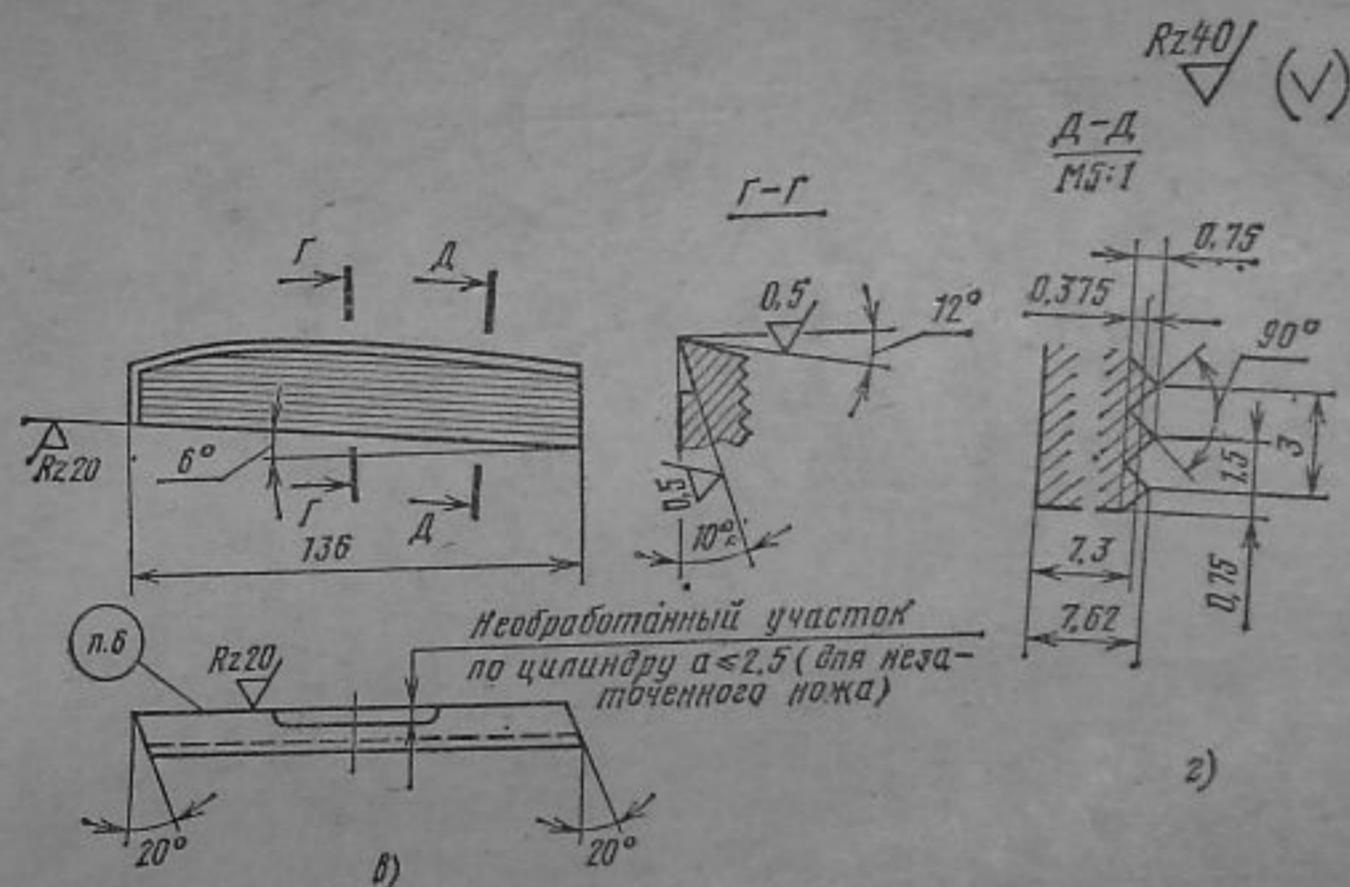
Чертеж сборной цилиндрической фрезы со вставными ножами:
